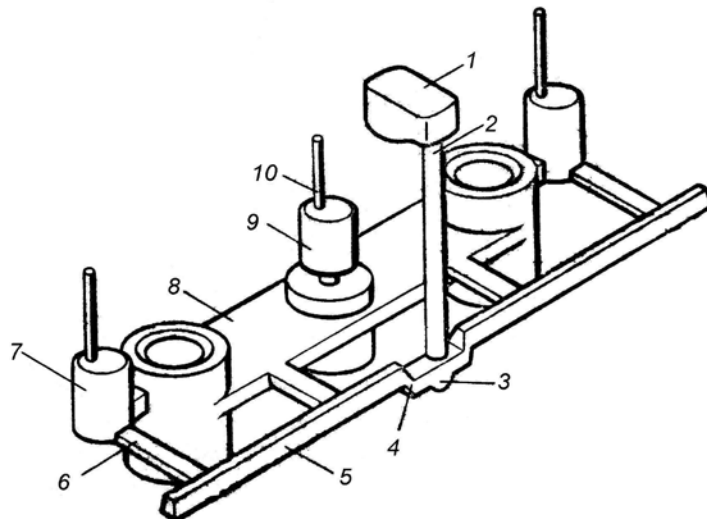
Отливка с литниковой системой: 1 – литниковая воронка или чаша, 2 – стояк, 3 – зумпф (углубление для частичного гашения динамической энергии потока металла), 4 – дрессель, 5 – шлакоуловитель, 6 – питатель, 7 – прибыль (боковая проливная), 8 – отливка, 9 – прибыль (верхняя), 10 – выпор
